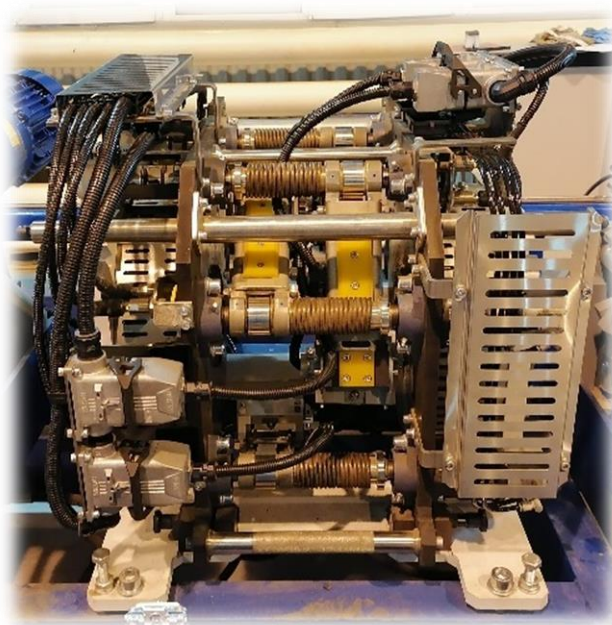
Общий вид установки магнитного контроля «MagnetoScan-3000»
